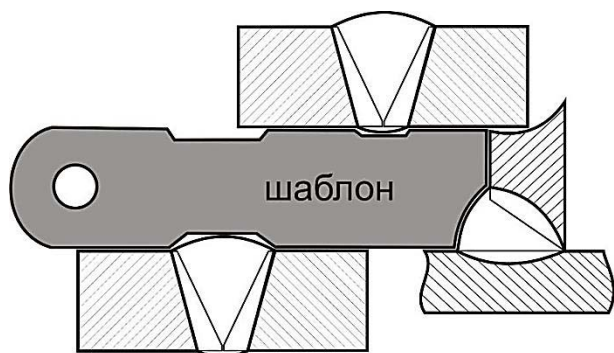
Специальный шаблон для контроля сварных швов
